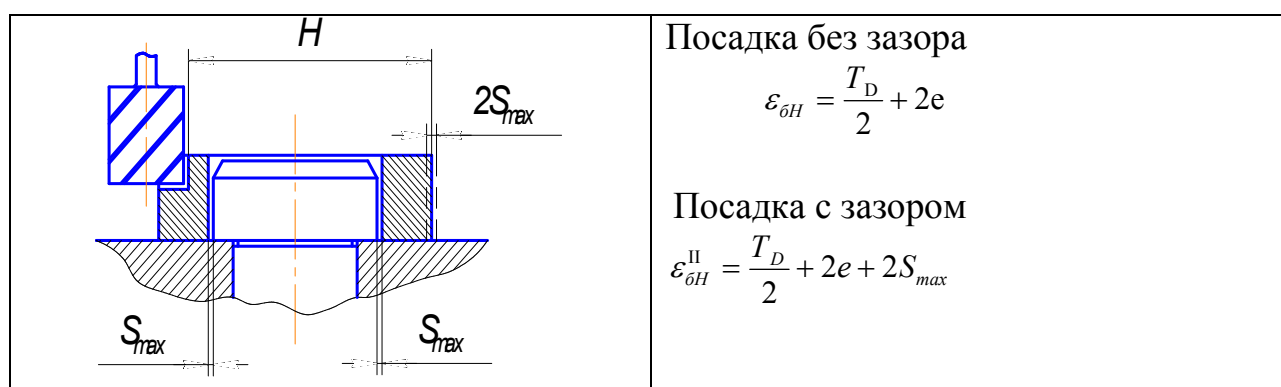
Схема для определения погрешности базирования размера Н цилиндрической заготовки, установленной на вертикальный палец установочный
